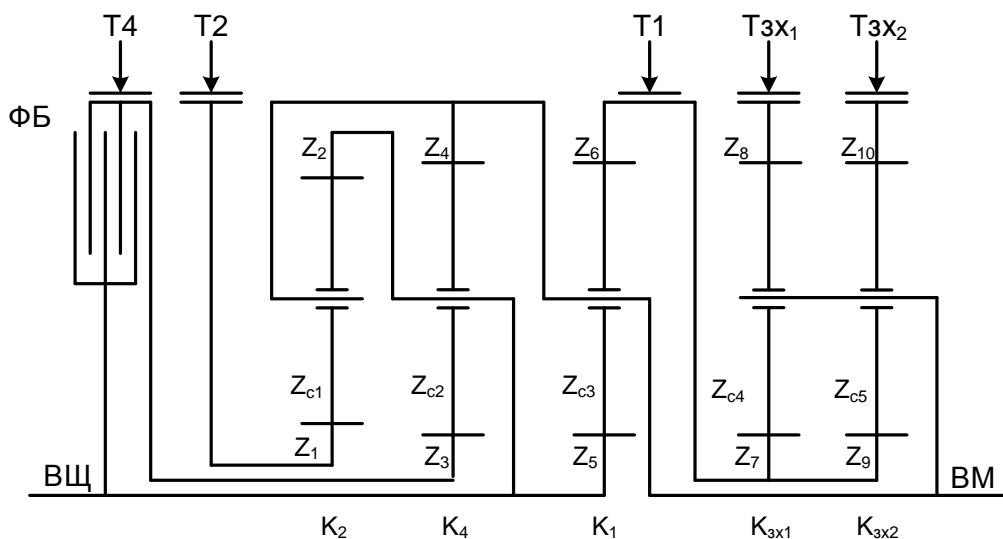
Вариант кинематической схемы планетарной коробки передач типа 4+2 с реверсом Вильсона
